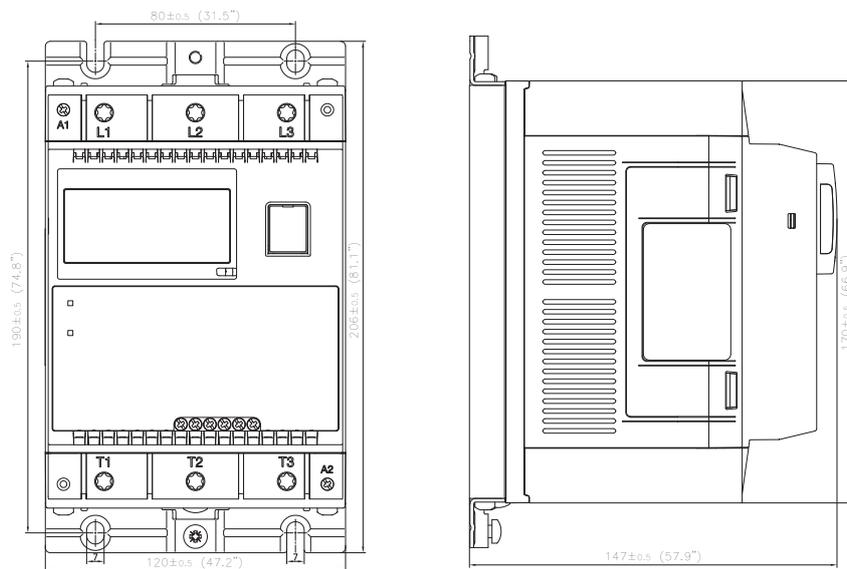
Versioni RSBT48.. (montaggio a pannello)
